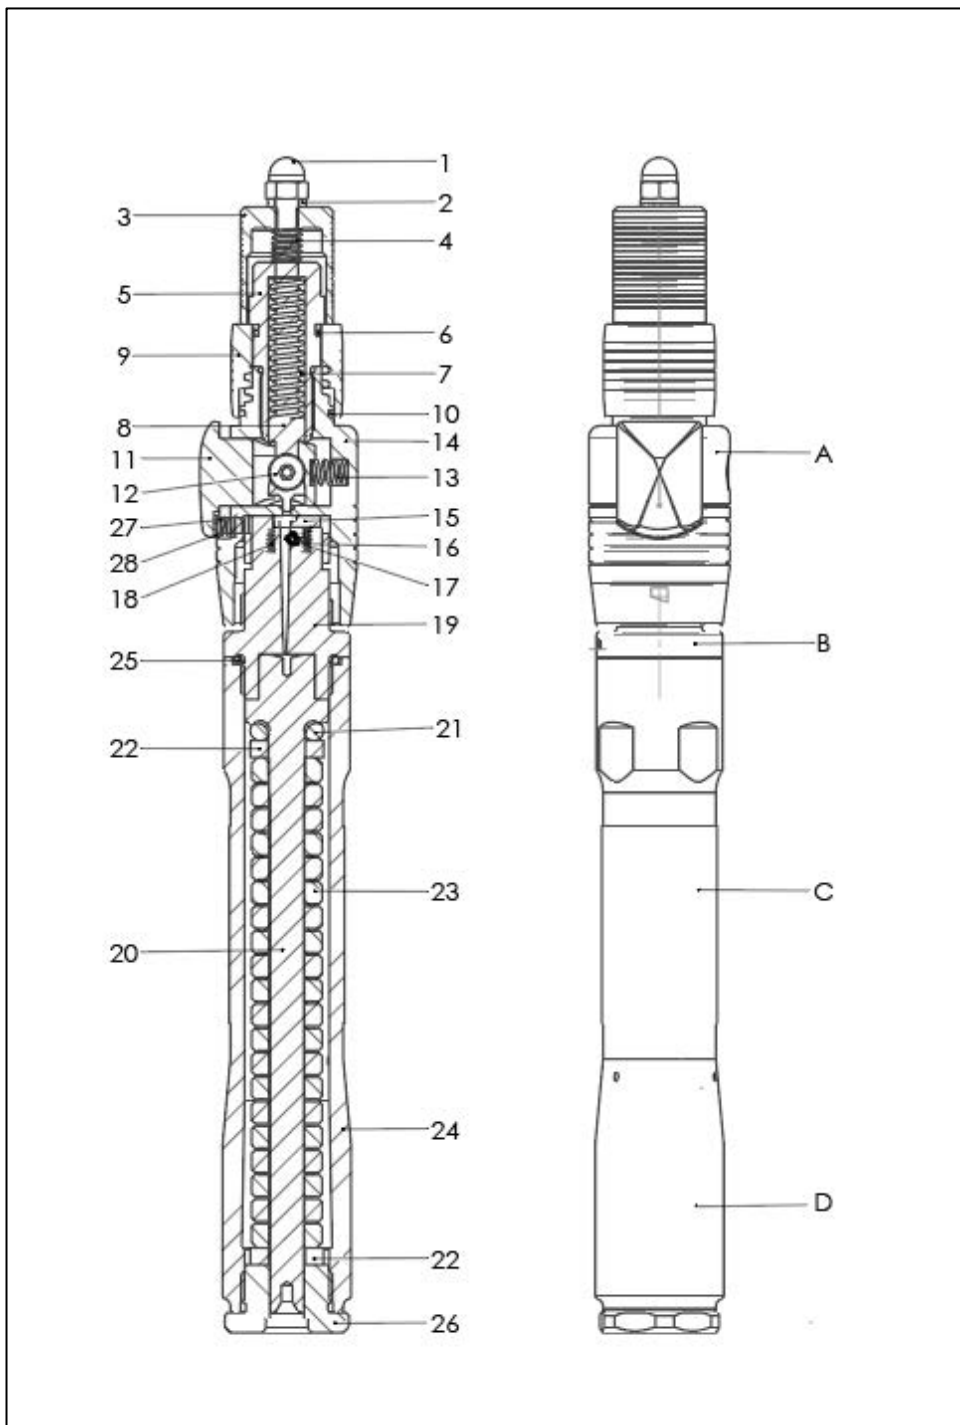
Baugruppen/Bauelemente Typ KLS
